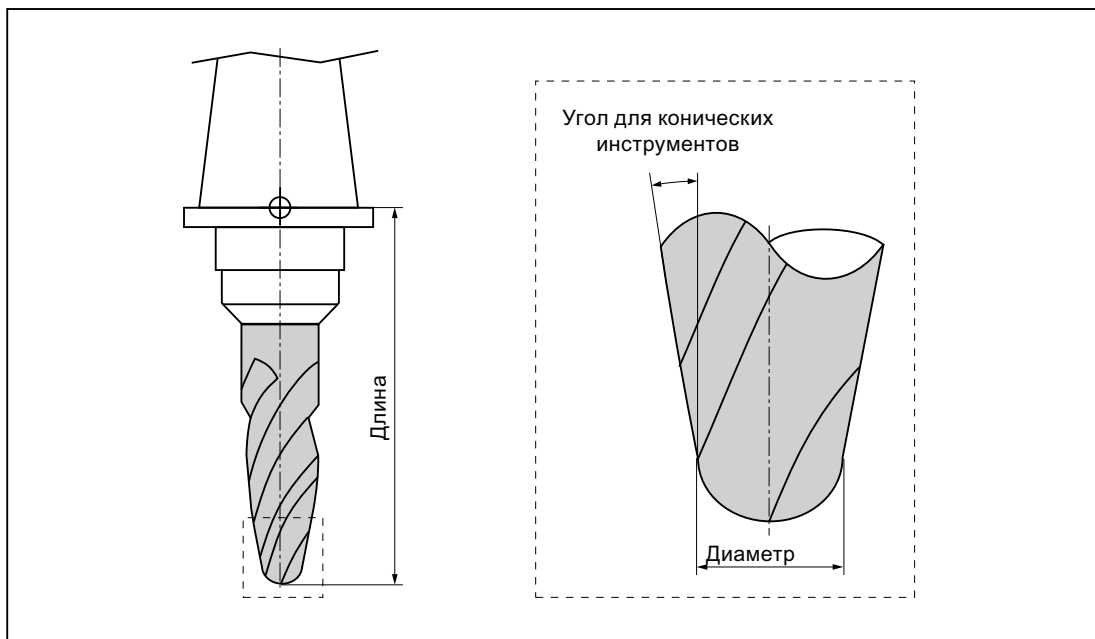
Инструмент 3D на примере конической концевой фрезы (тип 157)
